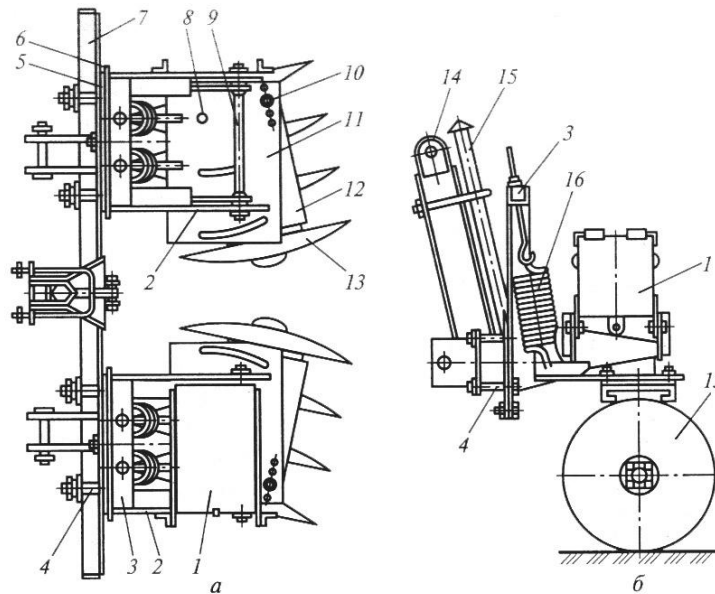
Культиватор лісовий борозенковий КЛБ-1,7
